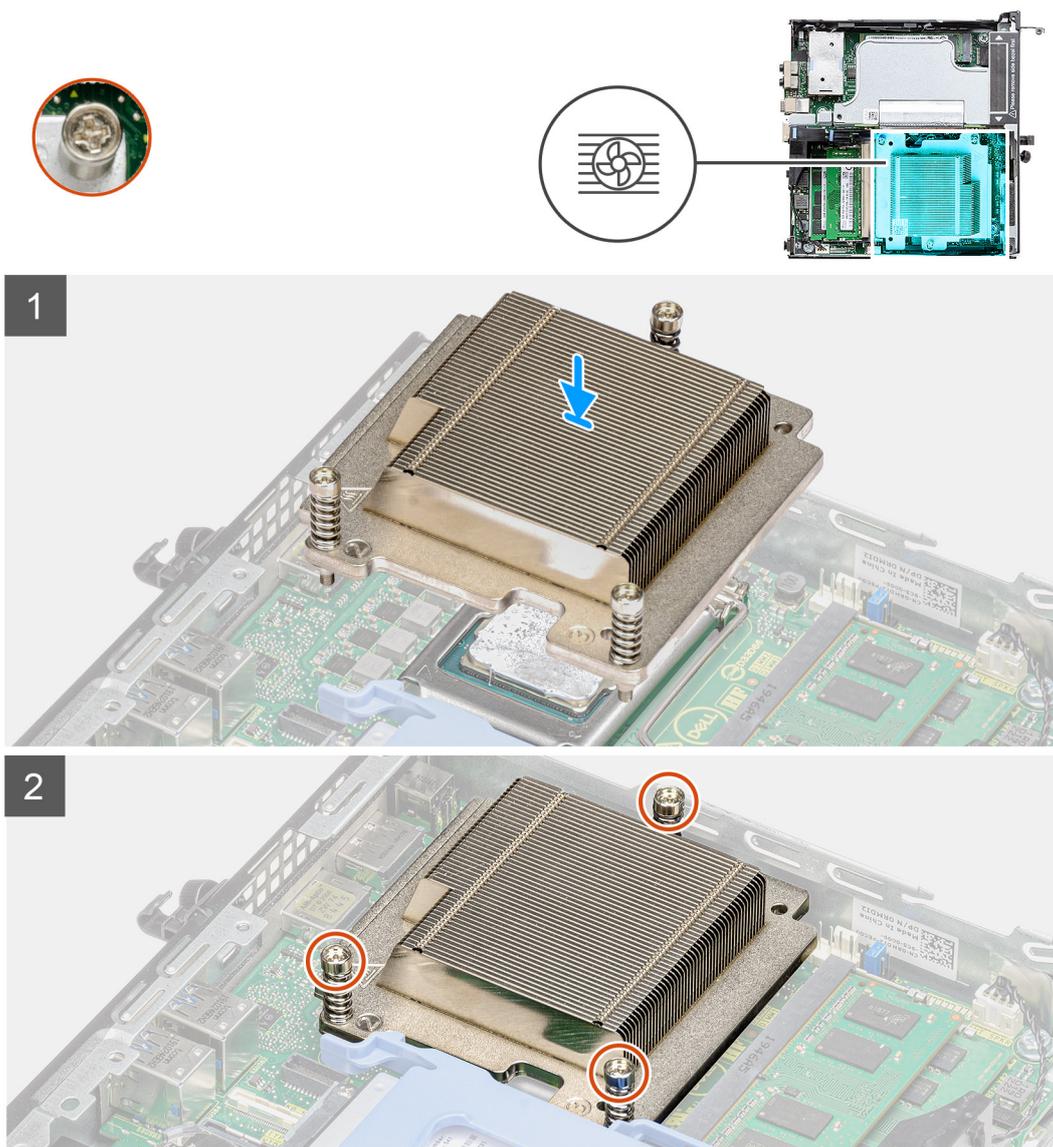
Dissipador de calor enviado com configuração do sistema com CPU de 65 W
